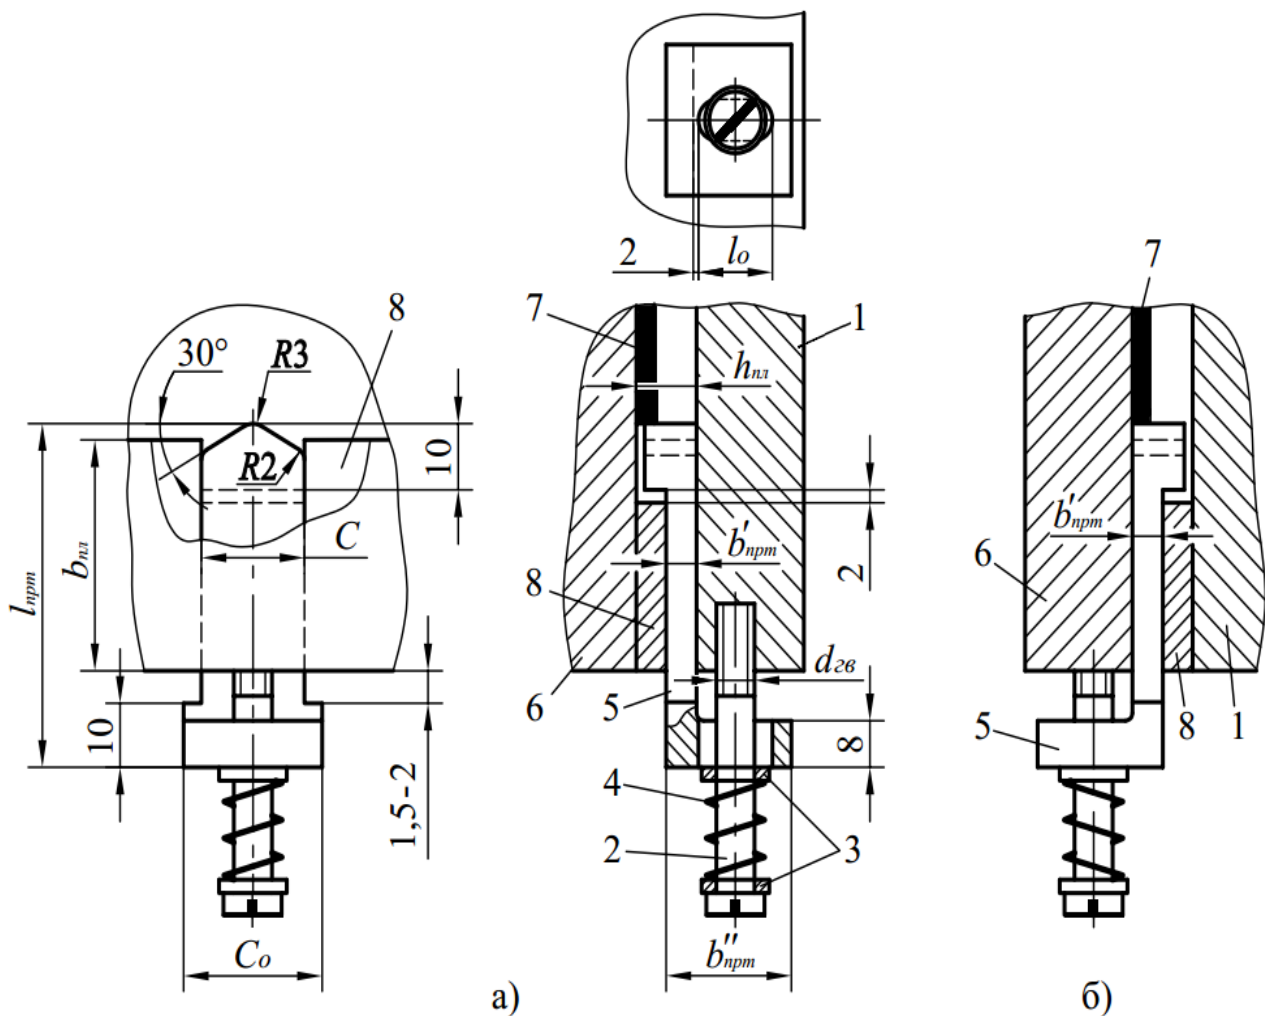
Конструкція напрямної планки з бічним притискувачем:
